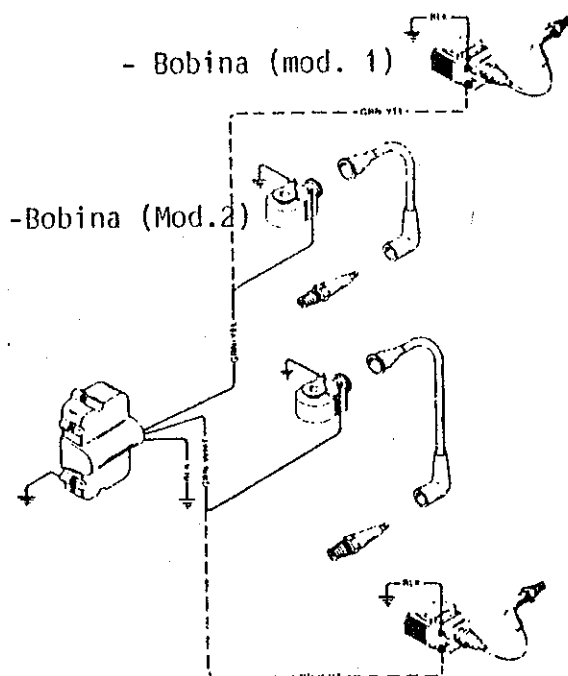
Bobinas de-encendido de motor de 2 cilindros.
